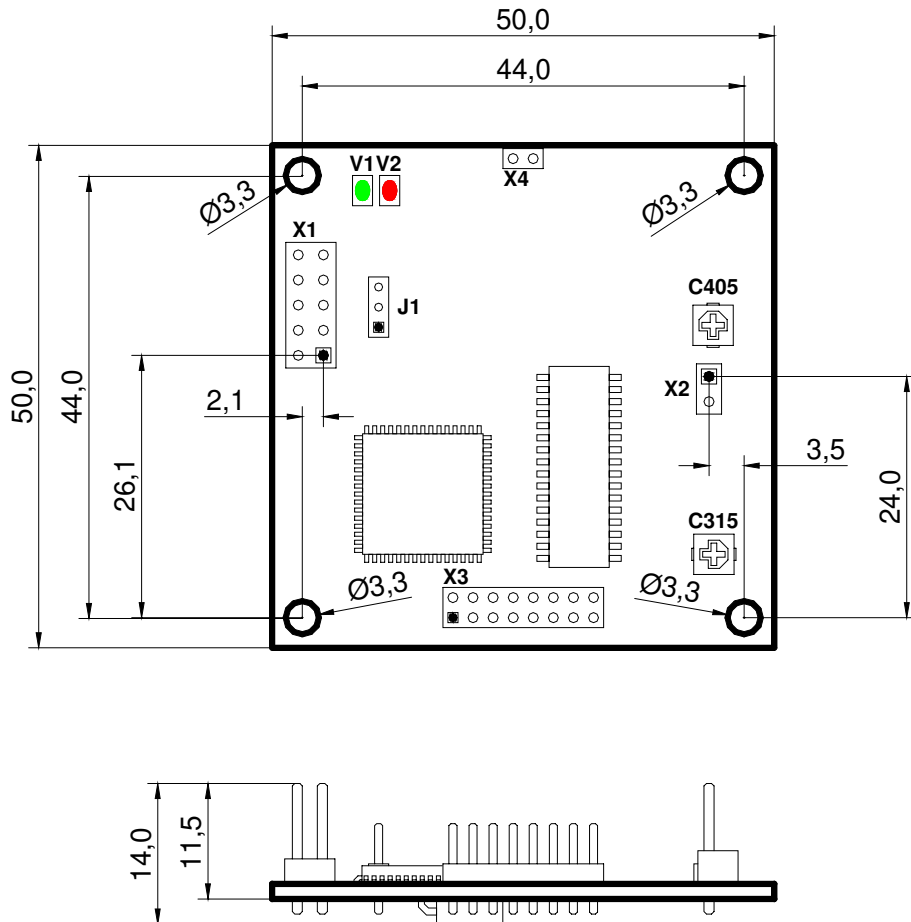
Maßzeichnung des Readermoduls ID CPR.M02
